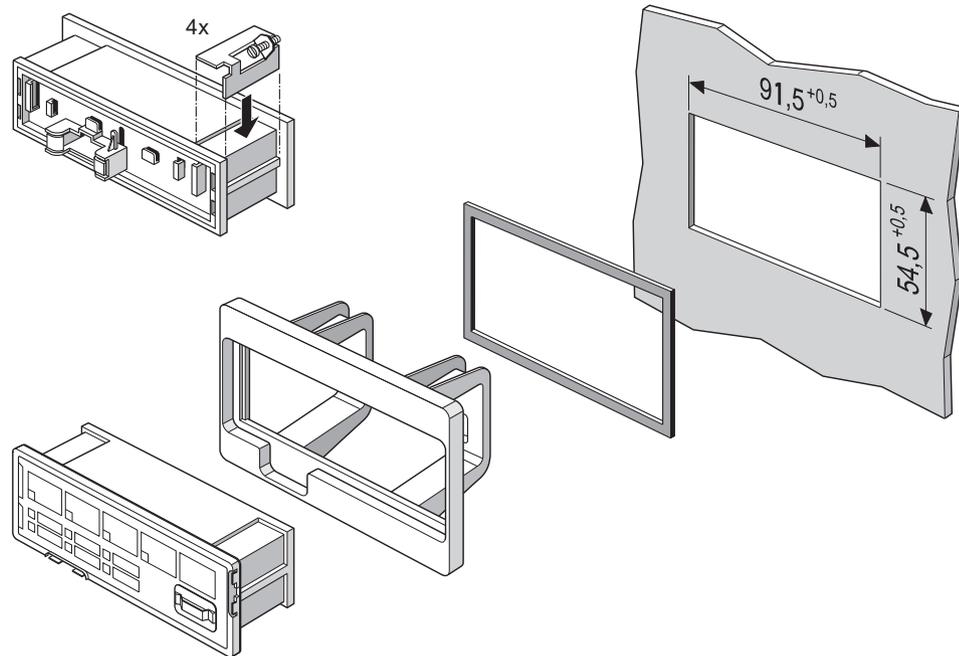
Montage de l'adaptateur pour module frontal (1)
